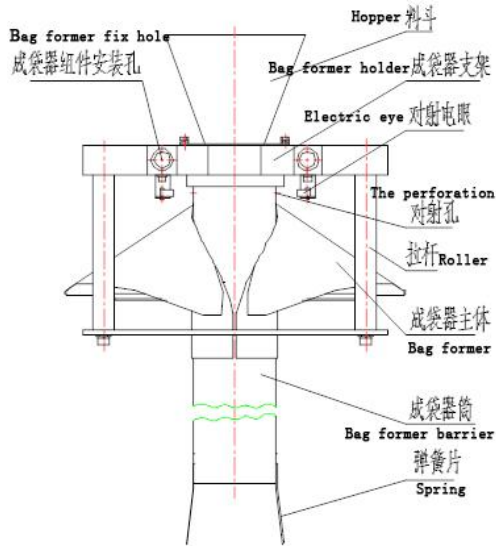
成袋器组件示意图 FIG. 32 diagram of bagger components
